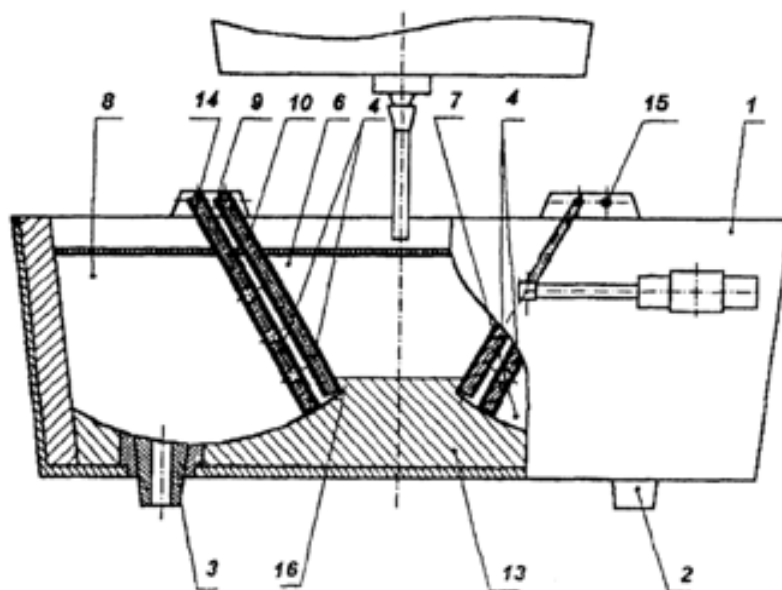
Промежуточный ковш для непрерывной разливки металла с подвижными перегородками
